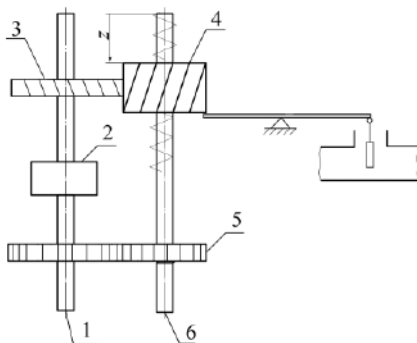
Регулятор Чиколева – Понселе: 1, 6 – валы; 2 – муфта; 3, 5 – шестерни; 4 – подвижная шестерня с пружинами
